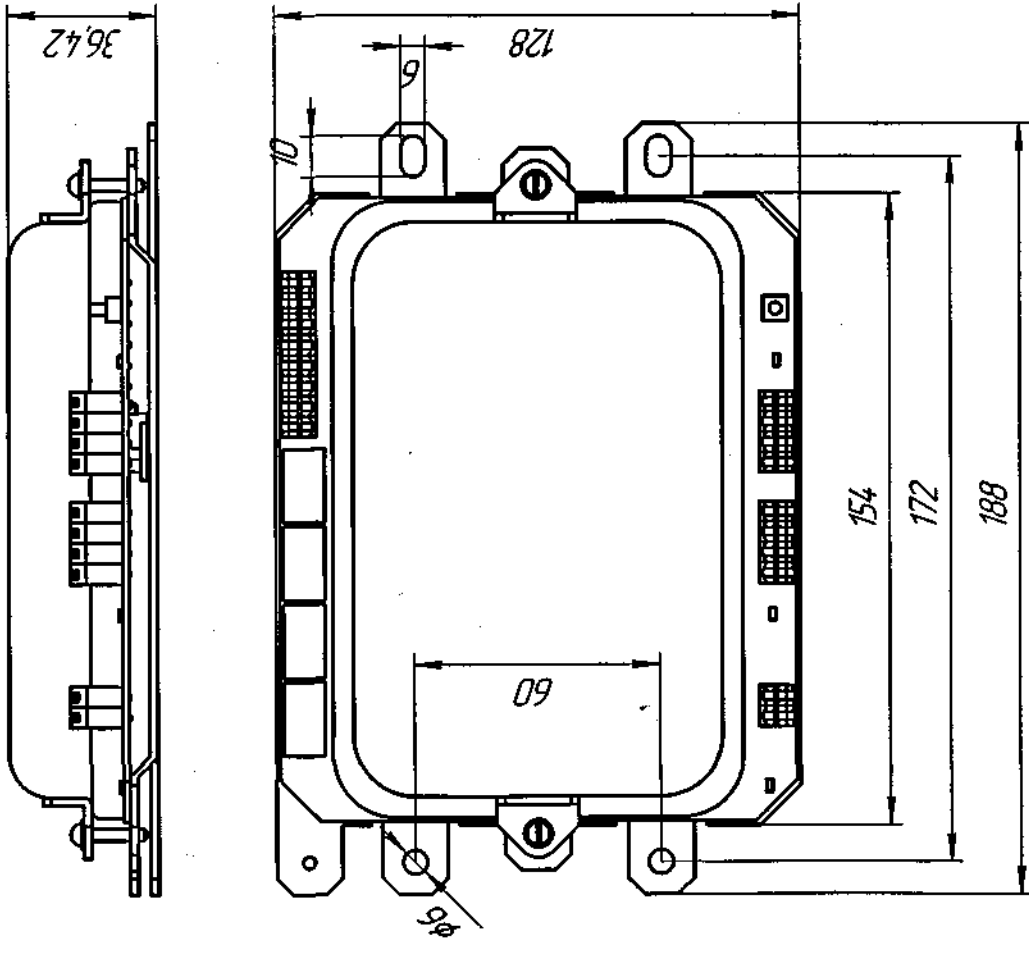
Блок логики для СУЛ — габаритный чертеж
